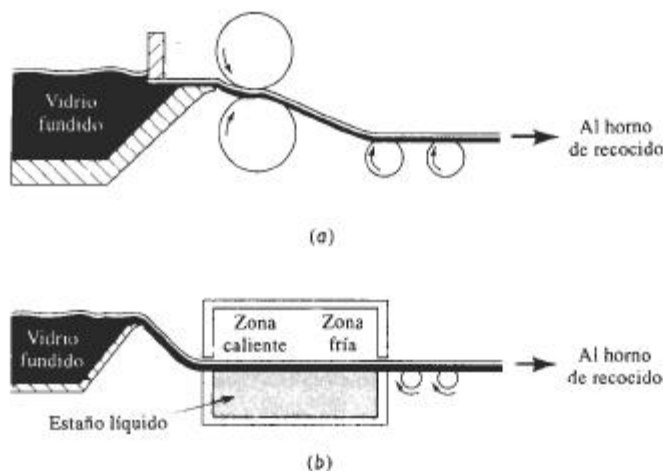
Técnicas para la manufactura de vidrio en hoja y en placa: (a) Laminado y (b) flotado del vidrio sobre estaño fundido.
